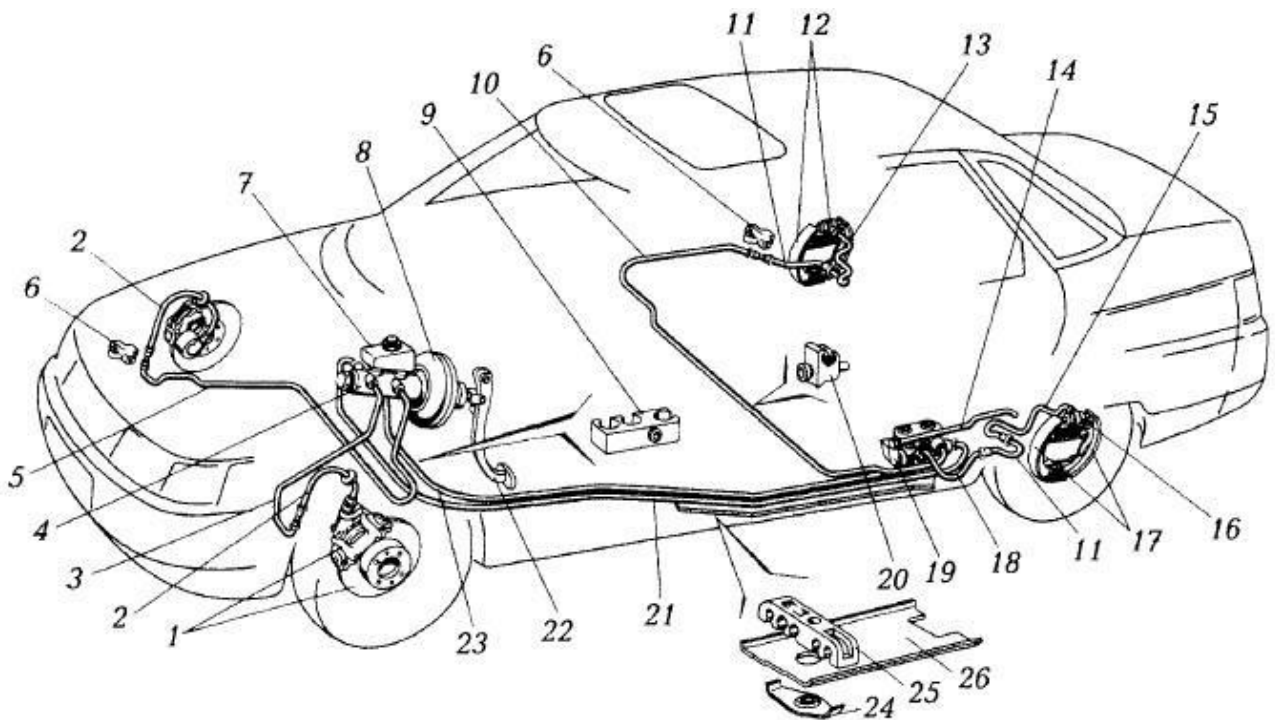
Схема компонування робочої гальмівної системи передньопривідного автомобіля ВАЗ
